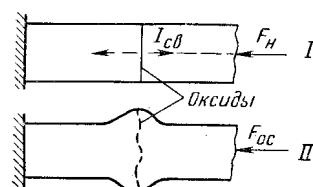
Схема образования соединения пристыковой сварке сопротивлением (F_h – начальное усилие; F_{oc} – усилие осадки).
